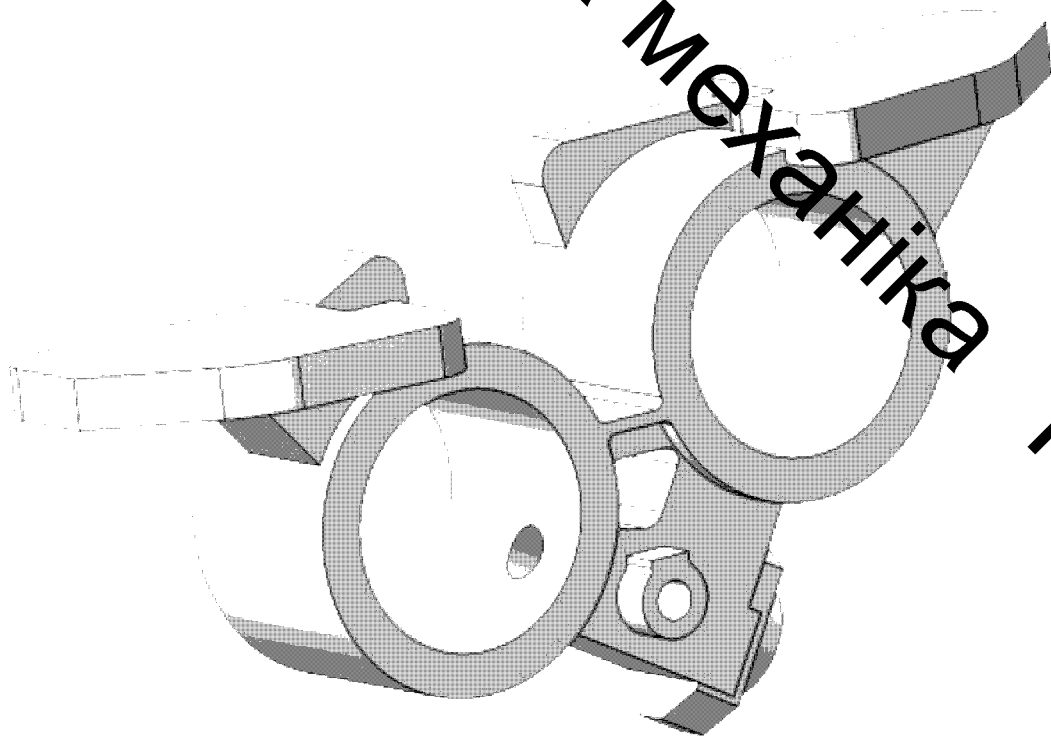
3D-модель заготовки, виготовленої литтям в піщано-глинисті форми
